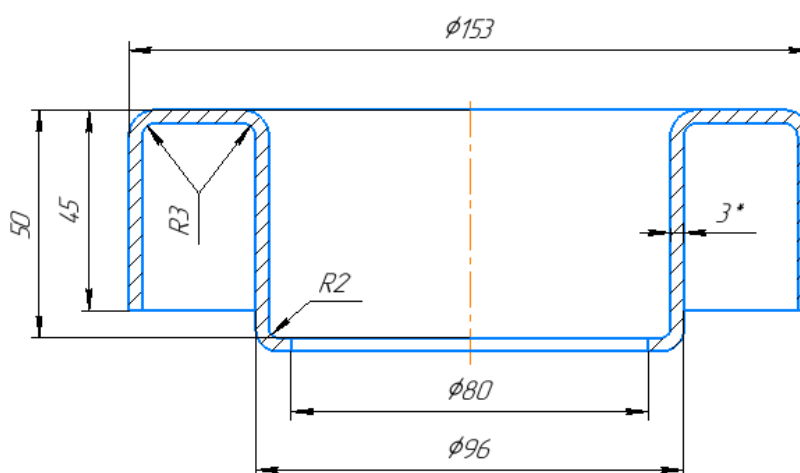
Эскиз заготовки после операции пробивки-калибровки
